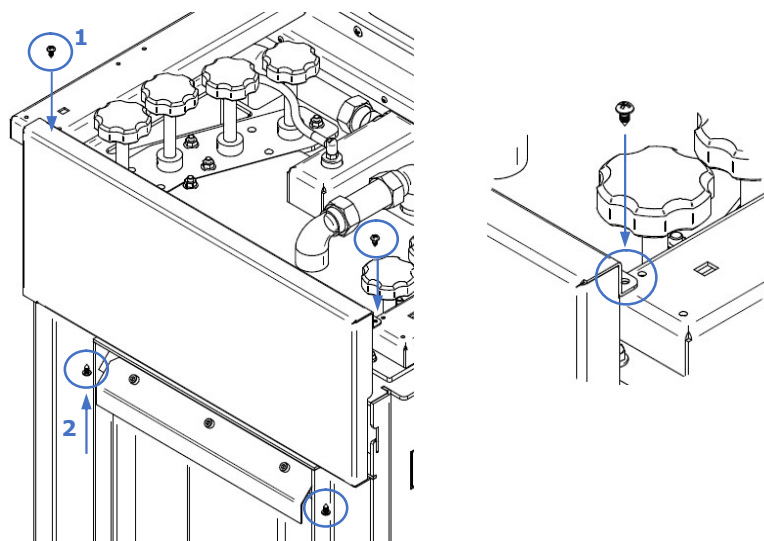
Montaje de la tapa frontal Hidro 17 kW y 23 kW
